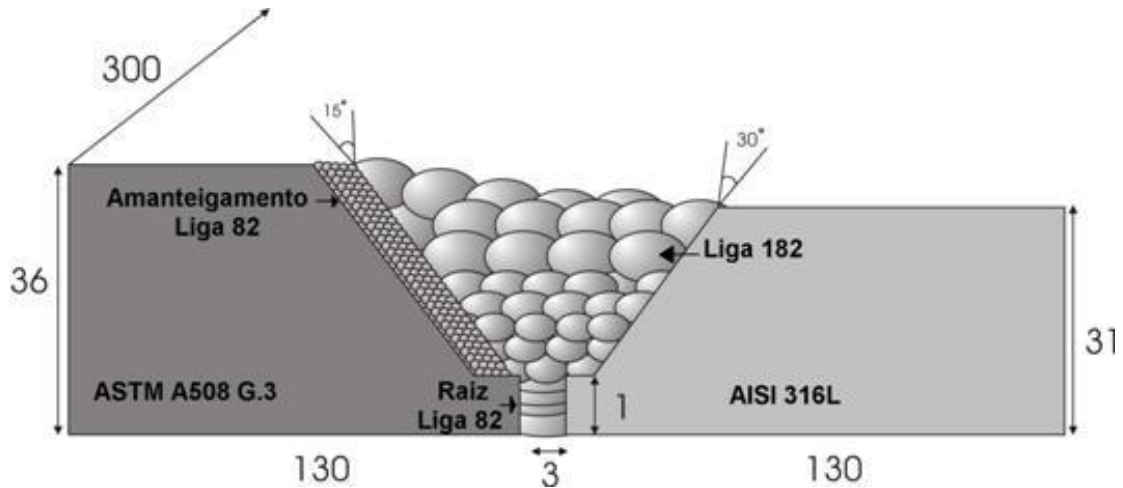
Representação esquemática da solda dissimilar entre o aço AISI 316L e o aço ASTM A-508 G3.
